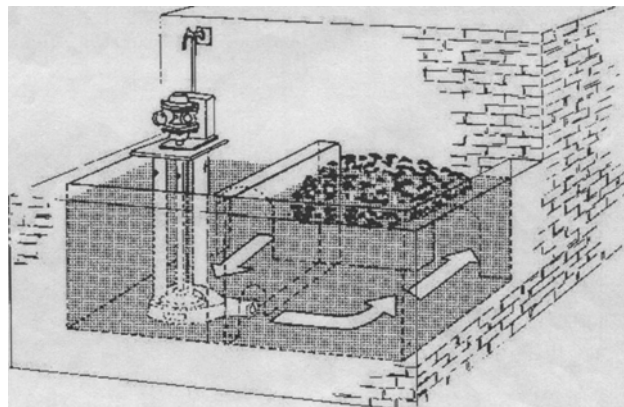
Схема процесу плавки металобрухту з розвинутою поверхнею за рахунок тепла розплаву, що циркулює під дією механічного насоса (The Carborundum Company Refractories & Electronics Division Metallurgies Branch)
